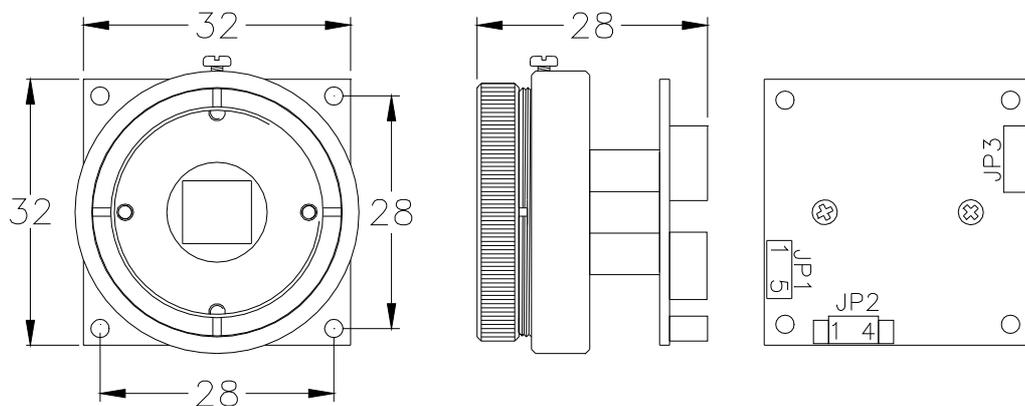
mechanische Abmessungen VCAM-002-3, Anschlußbelegungen
